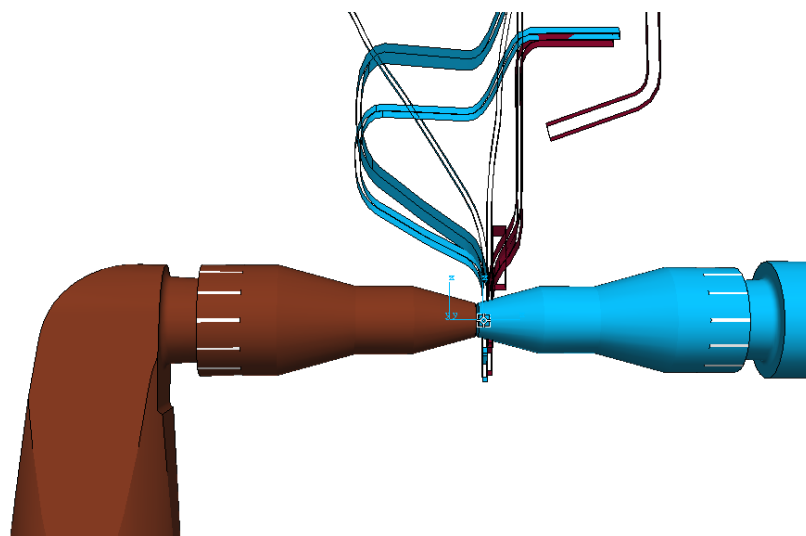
Сечение точек контакта сварочного пистолета и автодетали
